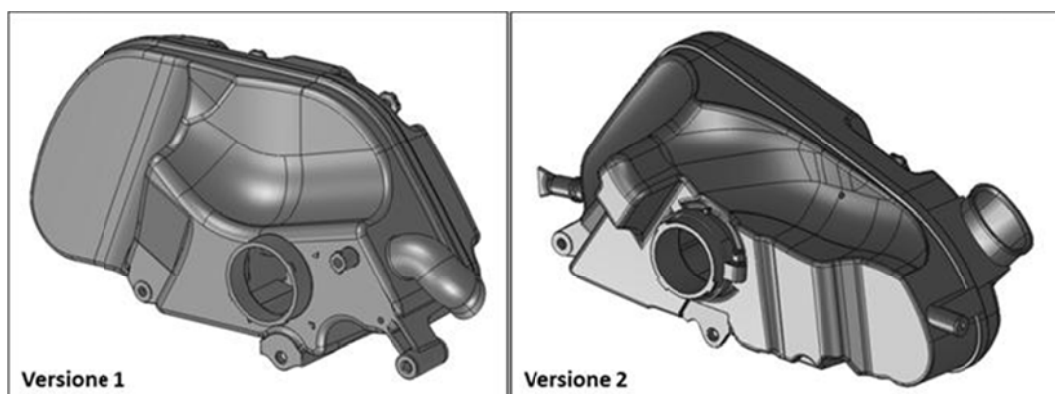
CAD del filtro nella versione motore 1 e nella versione motore 2
